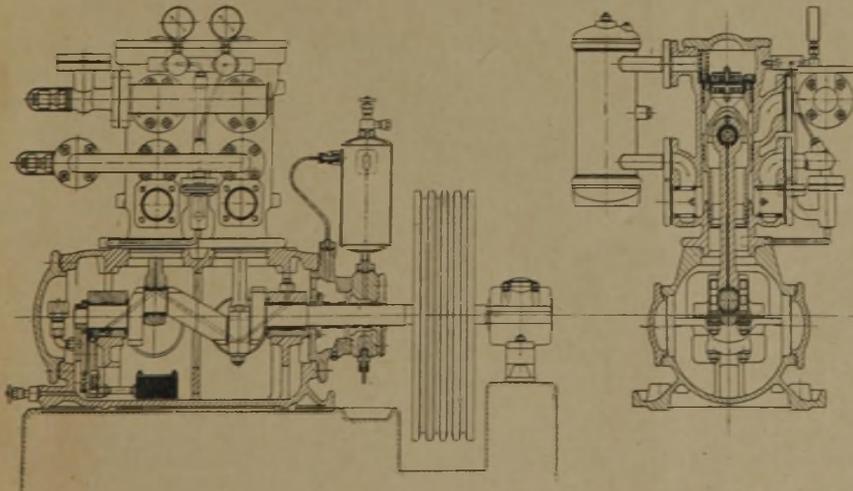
Kältemaschinenaggregat für die Bewetterung eines Schienenfahrzeuges
